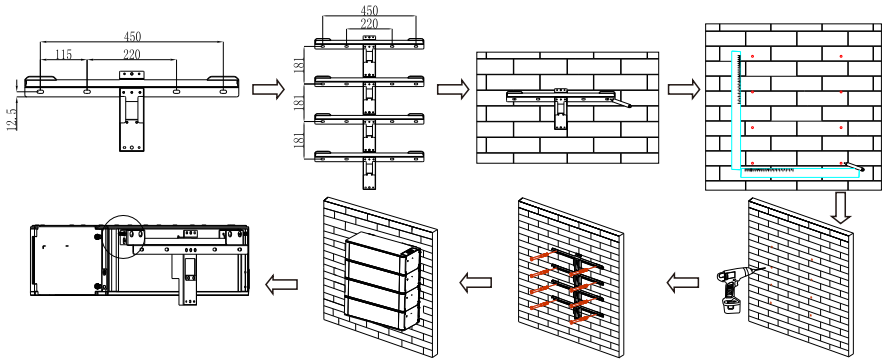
Installationsschritte für mehrere ARK 2.5L-A1
